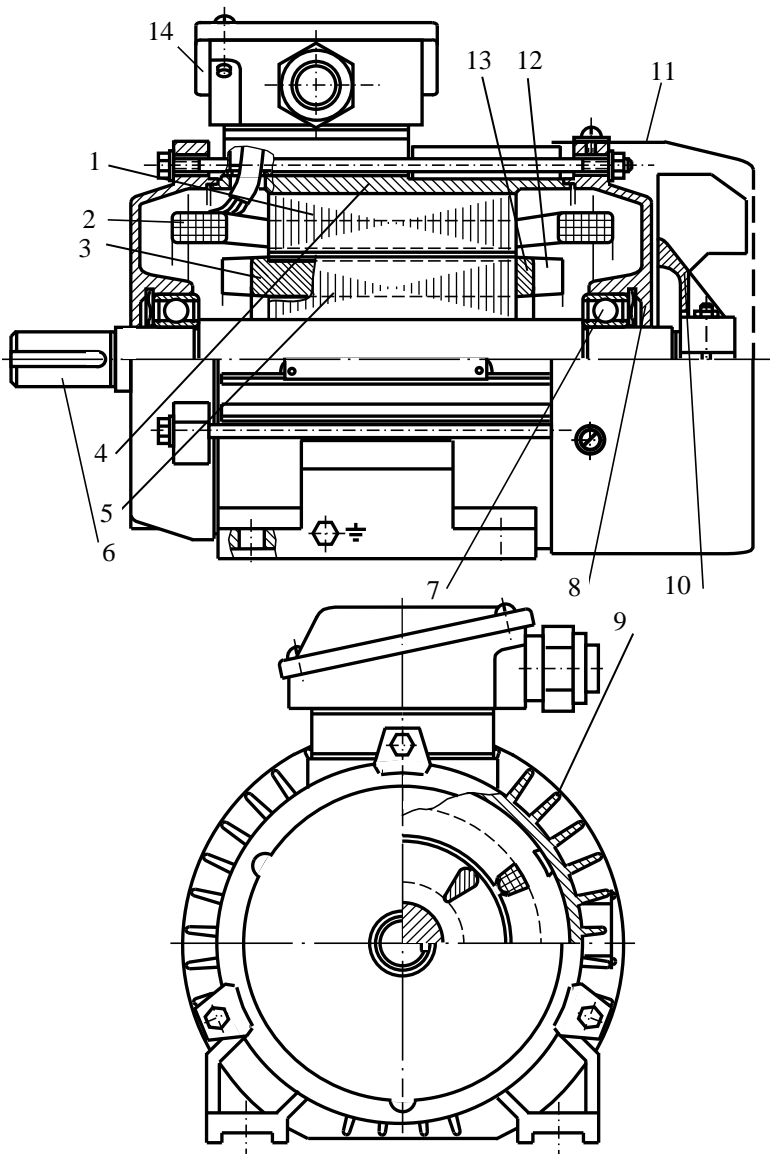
Асинхронный двигатель с короткозамкнутым ротором
